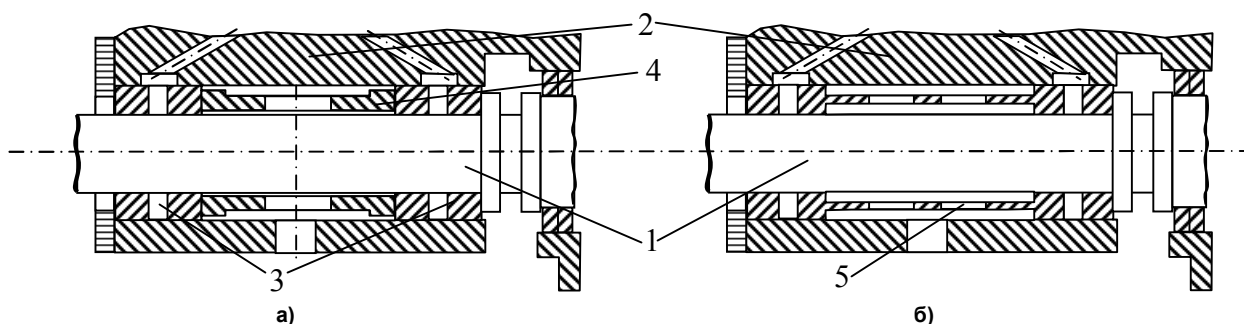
Конструкции подшипниковых узлов роторов турбокомпрессоров с ПВ втулками – а, с ПН моновтулкой – б: 1 – ротор, 2 – корпус подшипников, 3 – ПВ втулки, 4 – дистанционная втулка, 5 – ПН моновтулка
